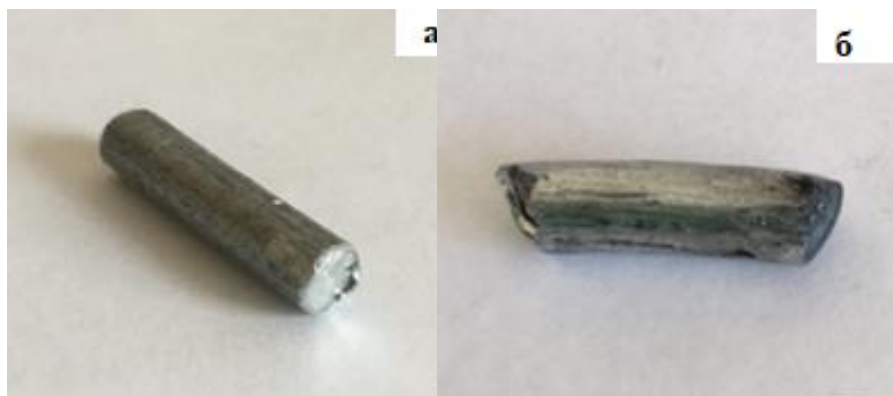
Вид исходной заготовки цинка для РКУП (а) и после одного прохода (б)
